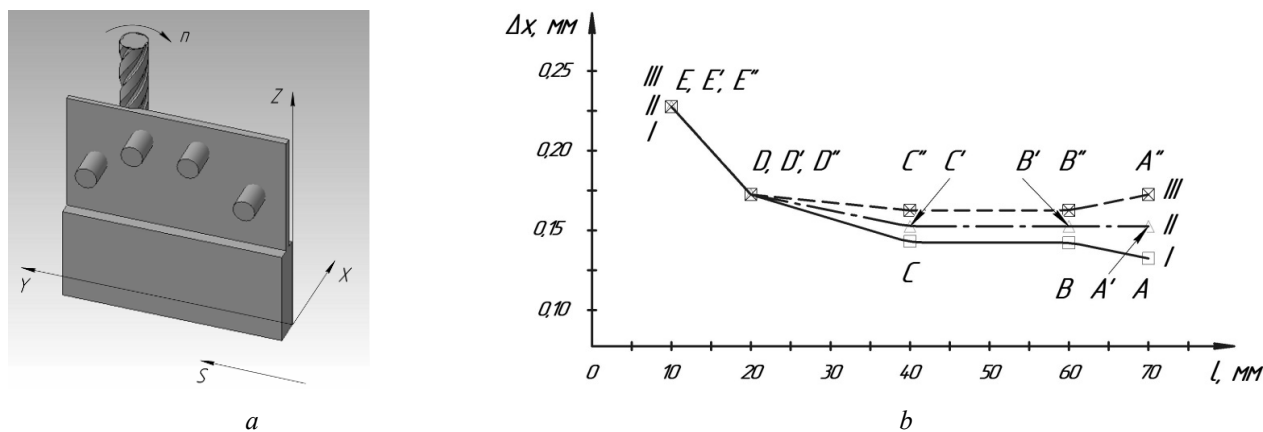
Схема фрезерования (а) и отклонение формы поверхности обработанной детали в сечениях I-I, II-II, III-II (b) с применением опорного модуля из 4 опор (положение опор изменено)
